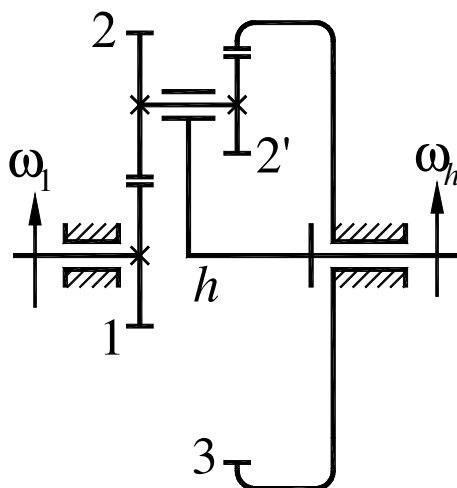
Планетарный механизм Джемса с двухвенцовым сателлитом:
